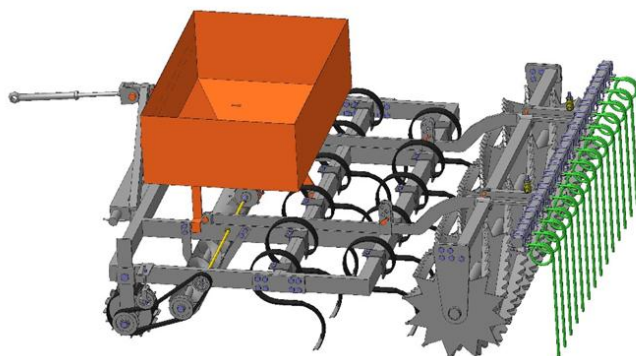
3D модель комбинированного почвообрабатывающего агрегата с внесением удобрений
